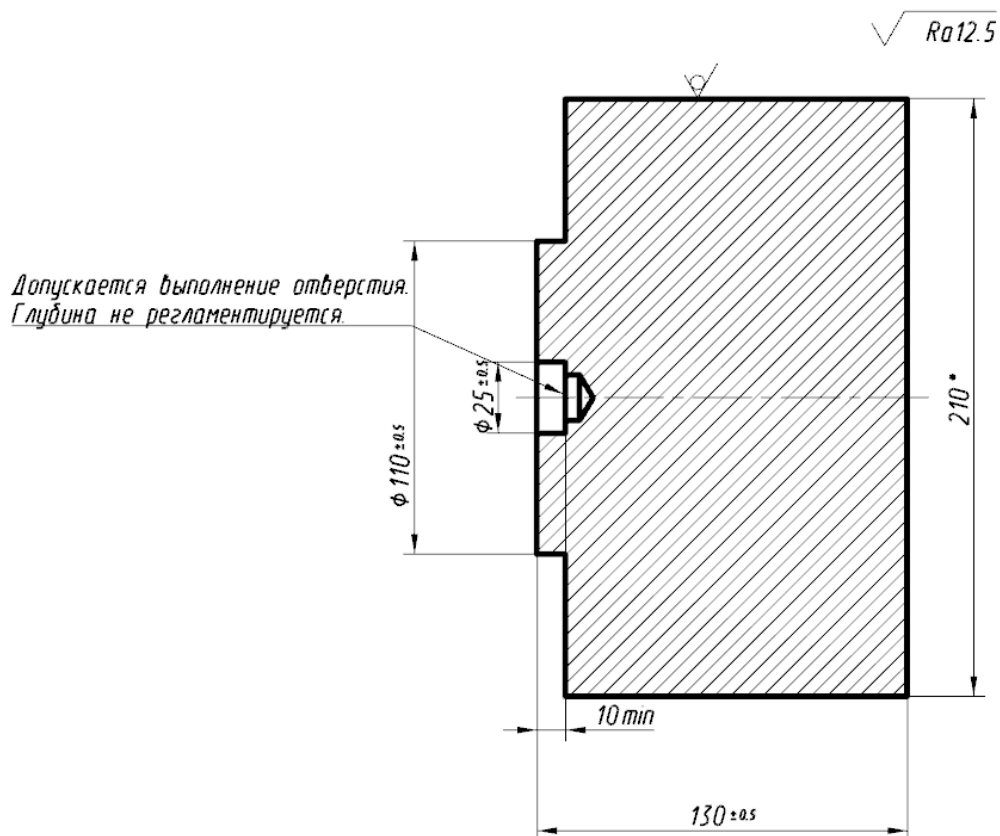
Чертеж выпилки образцов для испытаний (вид сбоку)
